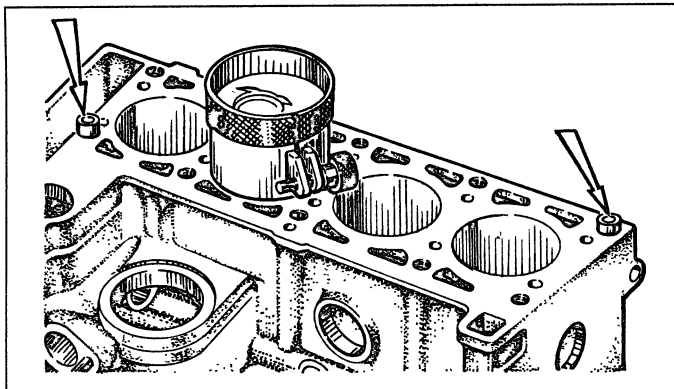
Установка поршня с поршневыми кольцами при помощи втулки для обжима колец и центрирующие втулки головки цилиндров (показаны стрелками)
